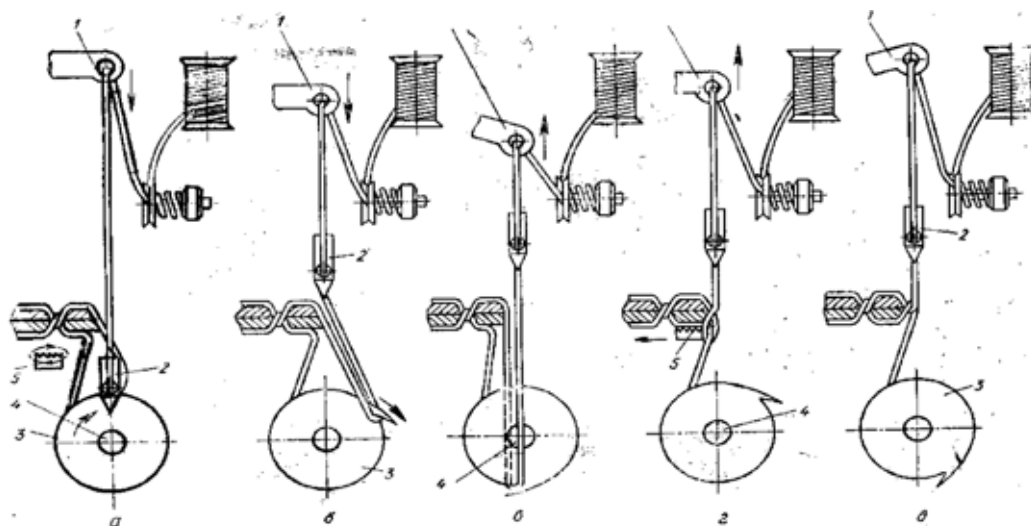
Положение нитепритягивателя верхней нити в процессе образования двухниточного челночного стежка
